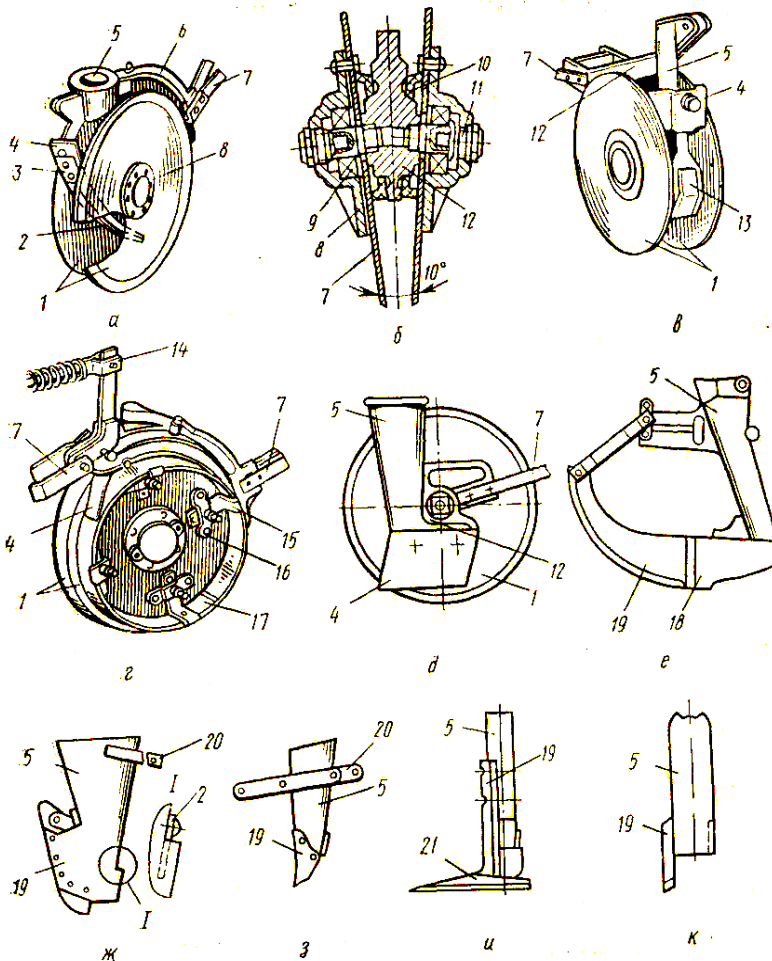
Типы сошников: а и б – двухдисковый рядовой; в - двухдисковый узкорядный; г – двухдисковый и ограничительными ребордами; д – однодисковый; е - полозовидный; ж – килевидный; з – анкерный; и – лаповый; к – трубчатый; 1 – диски; 2 – направитель семян; 3 – прижим; 4 – чистик; 5 – раструб (трубка); 6 – гребень; 7 – поводок; 8 - ступица; 9 - шарикоподшипник; 10 – резиновый уплотнитель; 11 – болт; 12 – корпус; 13 – делительная воронка; 14 – штанга; 15 – угольник; 16 – скоба; 17 – реборда; 18 – щека; 19 – наральник; 20 – хомут; 21 – стрельчатая лапа
